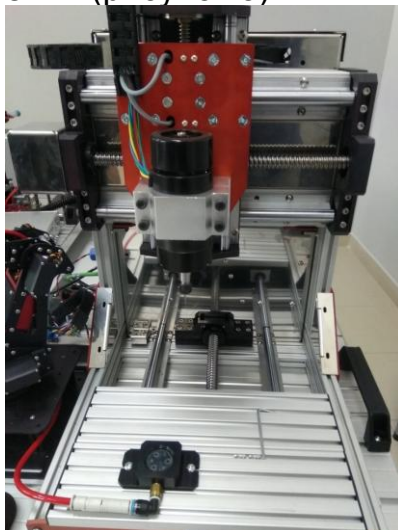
Трёхосевой фрезерный станок CNC MiniMILL
